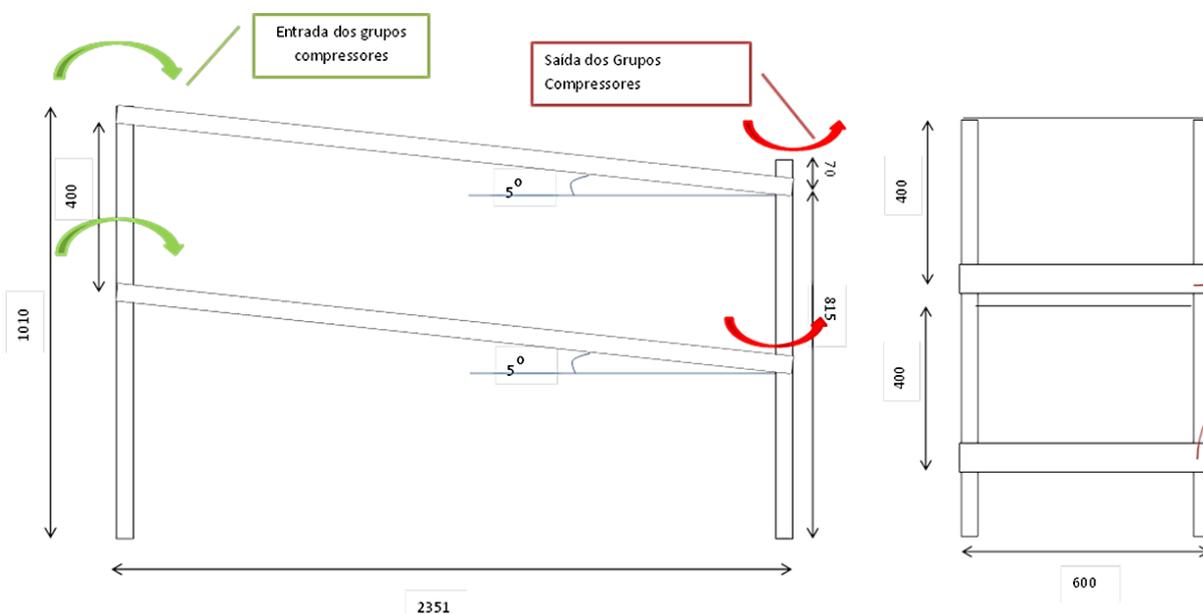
Projeto de Estantes de Supermercado Grupos Compressores, Vista lateral e Vista Frontal
